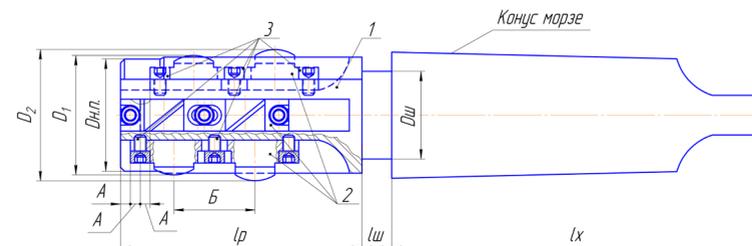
Общий вид резцовой сборной развёртки со двоянными безвершинными зубьями с разными диаметрами
